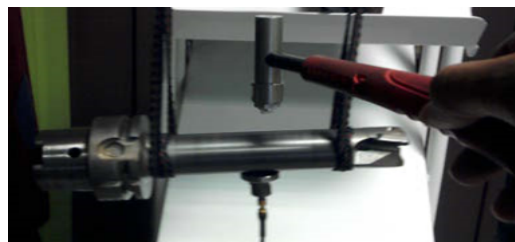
Essai d'impact au marteau sur outil en configuration libre
